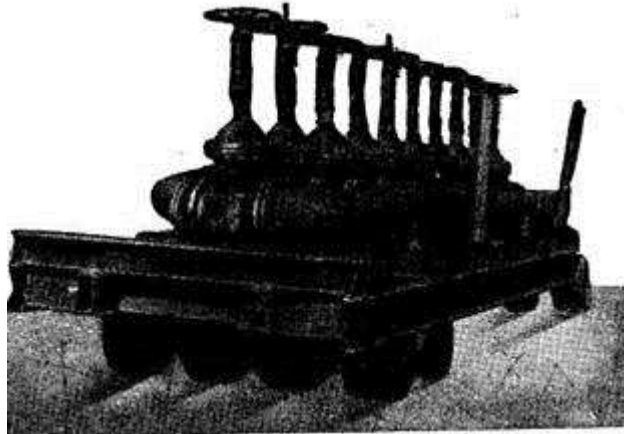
Перевозка узла с арматурой на трайлере
